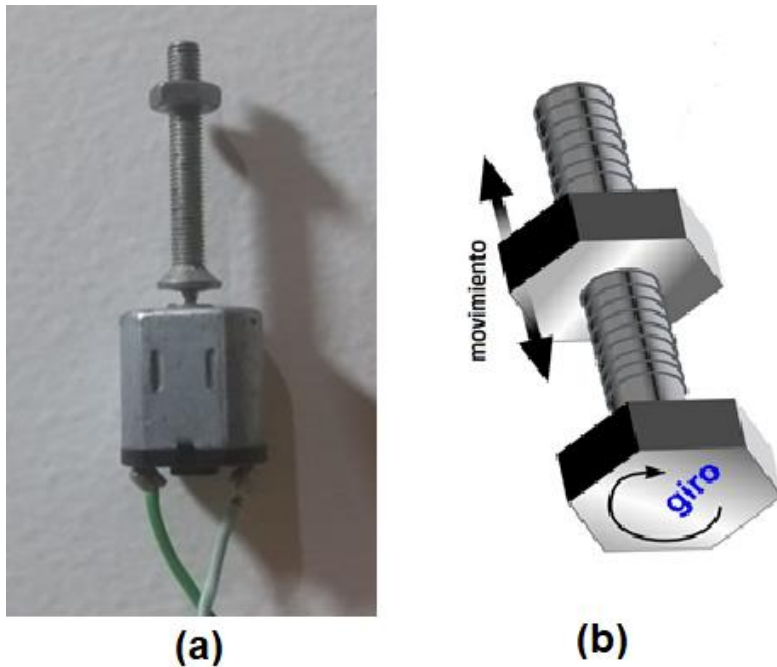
Tornillo ensamblado en el mini motor DC.
